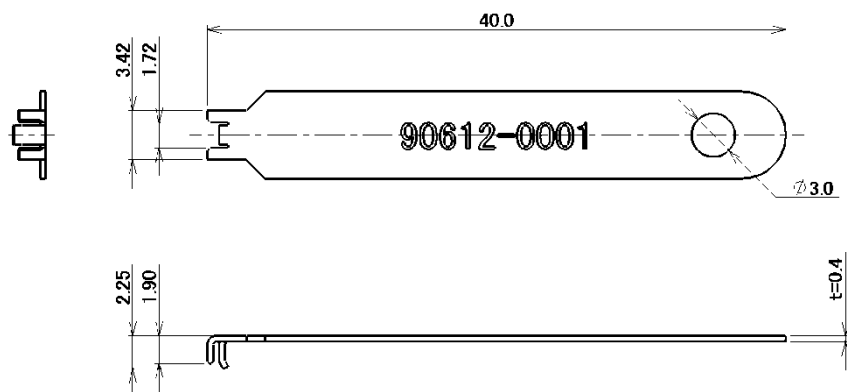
推奨 挿抜 JIG (Recommended Pushing and Pulling JIG)
